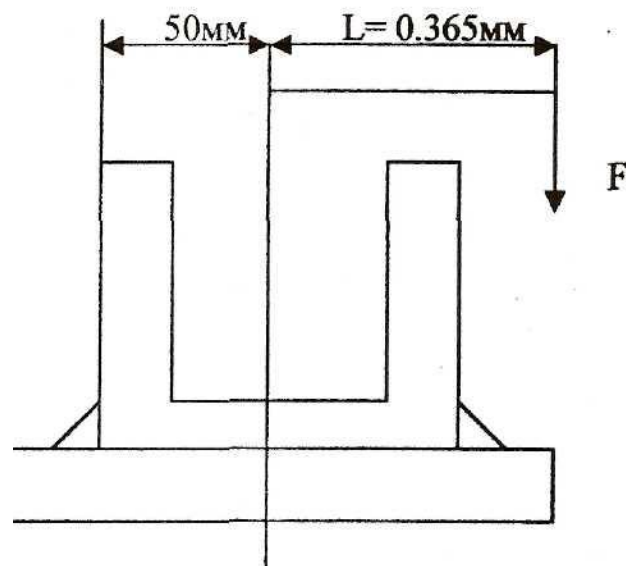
Сварочное соединение кронштейна с пластиной
